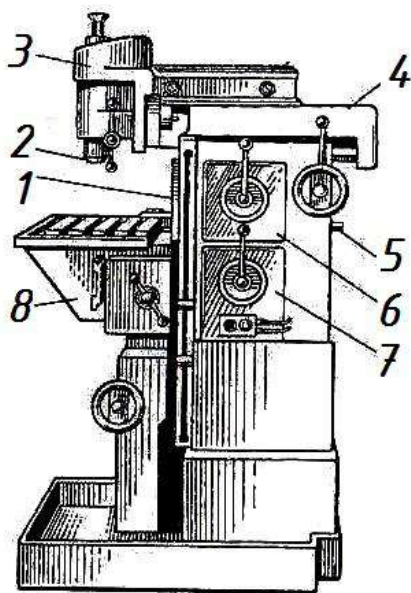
Широкоуніверсальний фрезерний верстат 679
